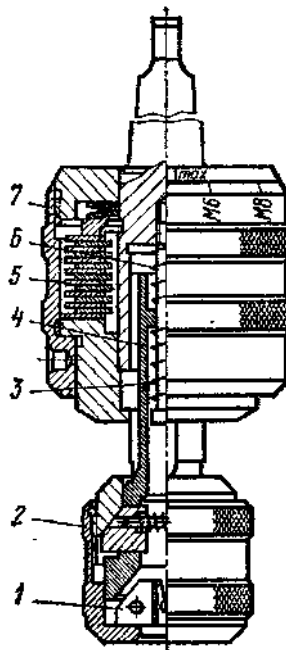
Різьбонарізний патрон з конусом Морзе для верстатів з ЧПУ свердлильно-фрезерної групи
